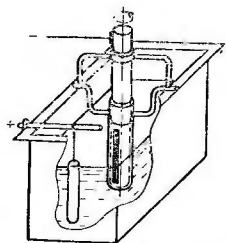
Установка для размерного никелирования цилиндрических поверхностей
